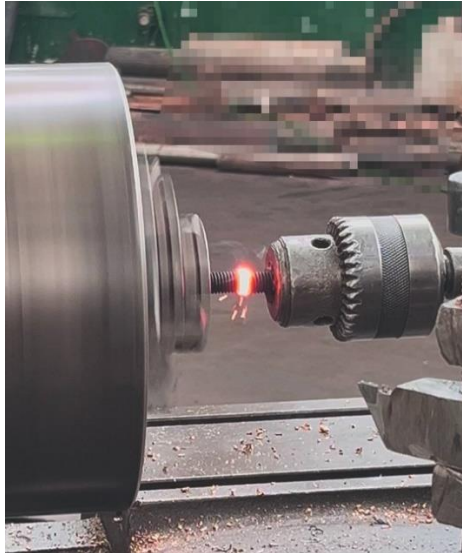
Soudage par friction rotative (RFW)
